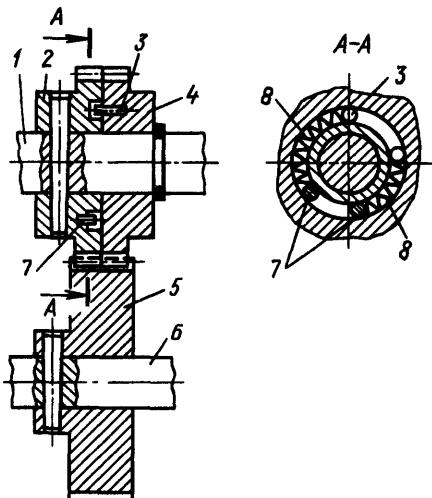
Беззазорная зубчатая передача с выборкой зазора пружиной круглого сечения
